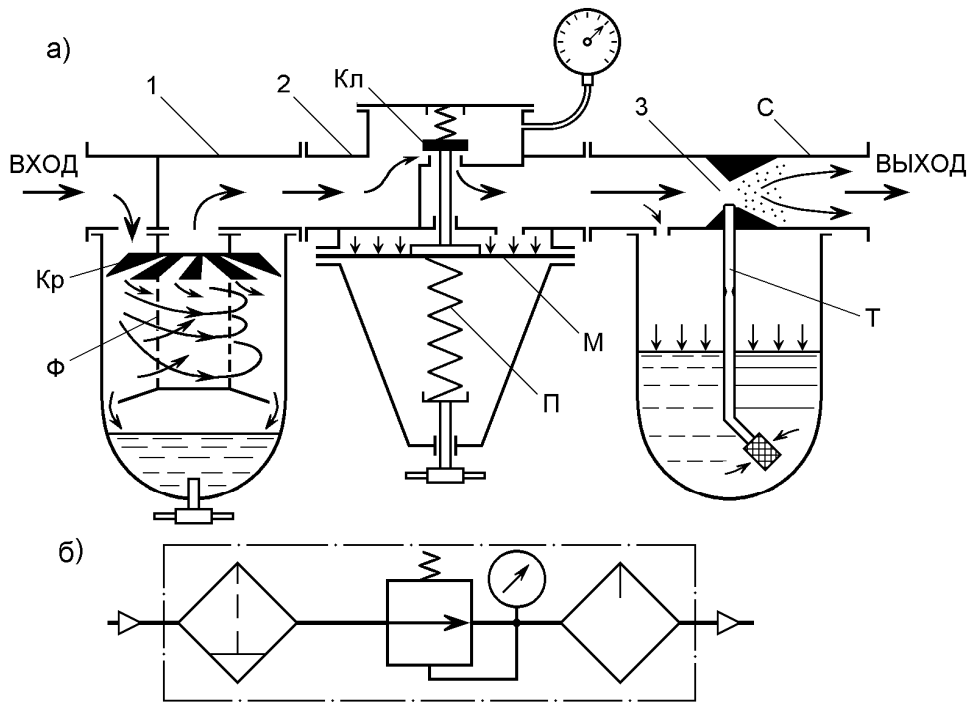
Типовой узел подготовки воздуха и его обозначение
